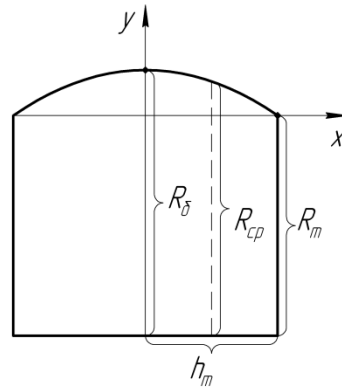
Розрахункова схема для аналітичного опису форми бічної поверхні
